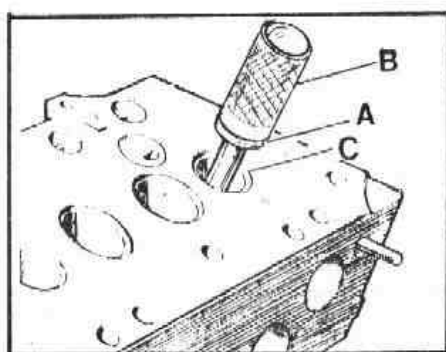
Montaje de asientos postizos de las válvulas de escape
